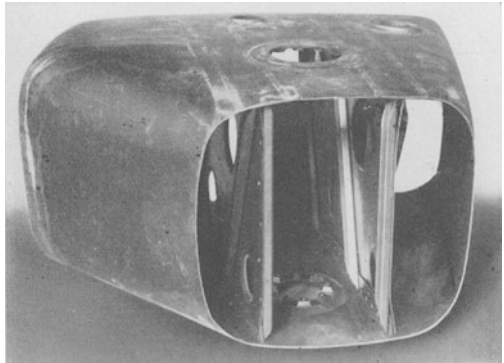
Flugzeugbenzintank aus Elektron, geschweißt.
